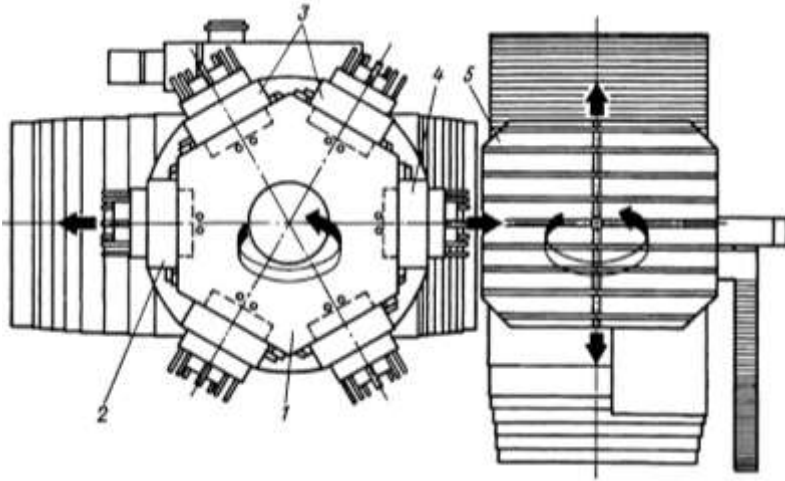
Багатоцільовий верстат із змінними багатошпindelними головками [39].
